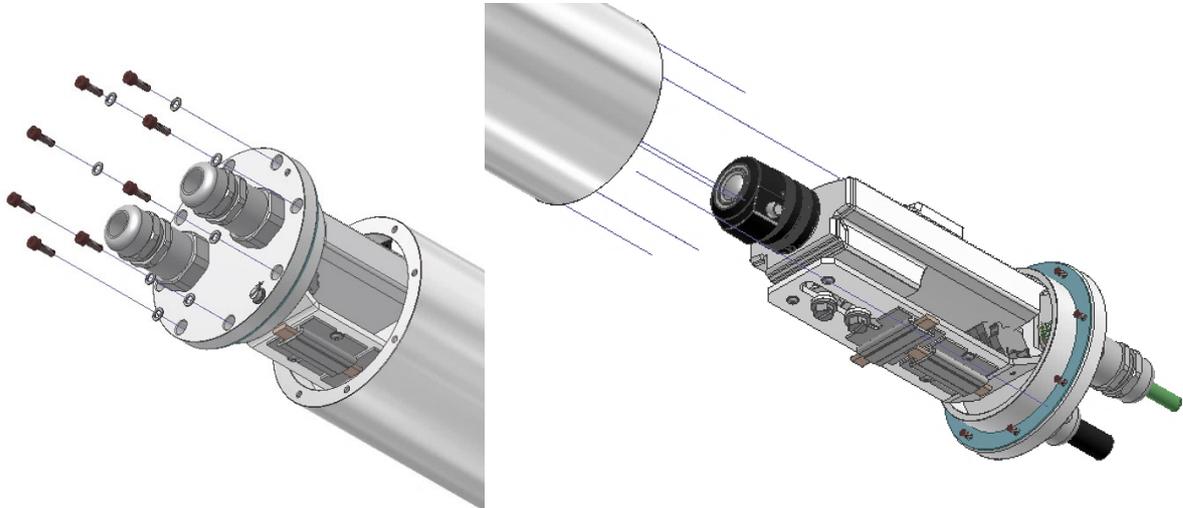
Öffnen der ExCam IPM1137-LE (Abb. ähnlich)
